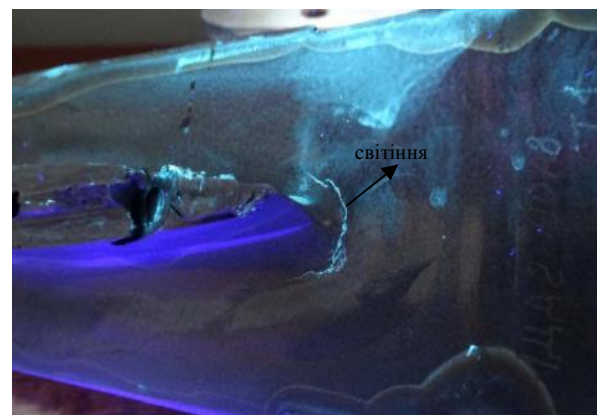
Індикаторний рисунок дефекту на проточній поверхні фрагменту зварного з'єднання стійки переднього корпусу двигуна РД-33.
